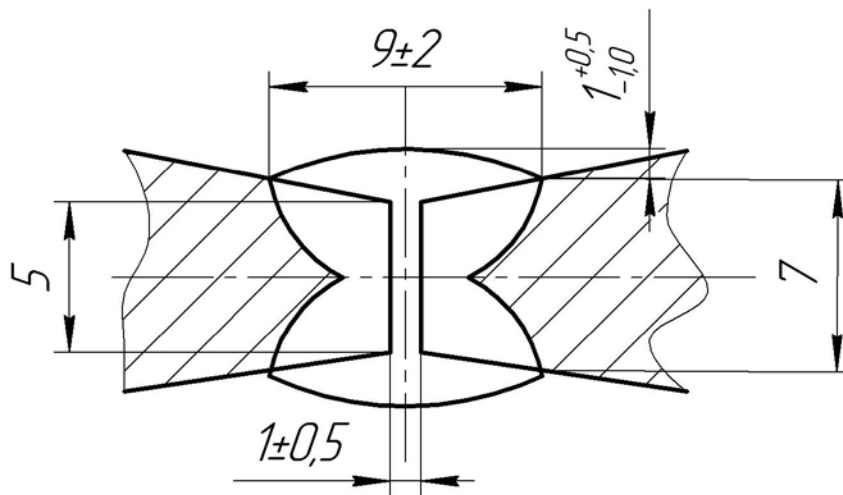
Экспериментальный данные сварного шва
